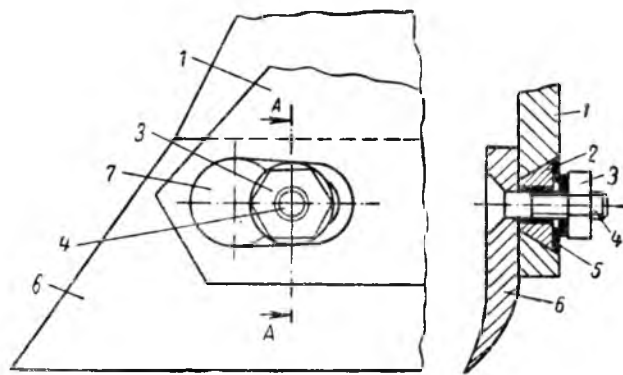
Предлагаемая схема крепления лемеха к корпусу плуга
